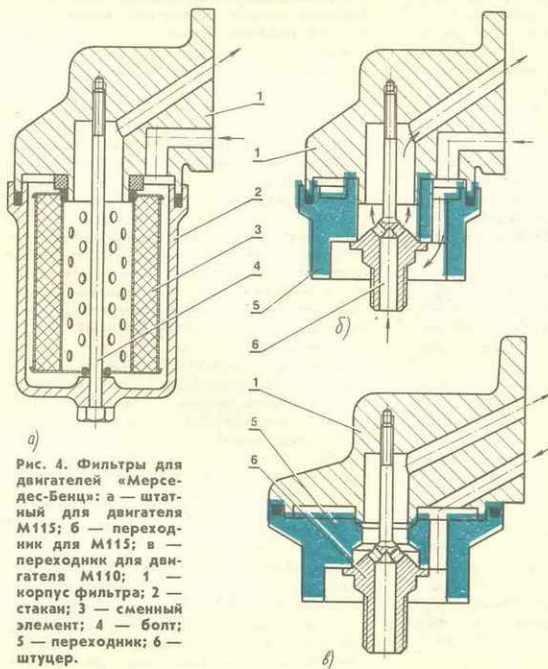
Фильтры для двигателей «Мерседес-Бенц»: а — штатный для двигателя М115; б — переходник для М115; в — переходник для двигателя М110; 1 — корпус фильтра; 2 — стакан; 3 — сменный элемент; 4 — болт; 5 — переходник; 6 — штуцер.
